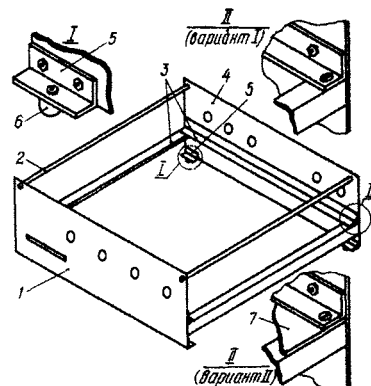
Устройство корпуса для крупногабаритных устройств: 1 — стенка передняя; 2 — стяжка, 2 шт., крепить к дет. 1 и 4 винтами; 3 — уголки, соединить друг с другом и с дет. 1 и 4 винтами; 4 — стенка задняя; 5 — уголок-держатель ножки, 4 шт., закрепить на дет. 1 и 4 винтами с гайками; 6 — ножка, 4 шт., закрепить на дет. 5 винтом с гайкой; 7 — панель.
